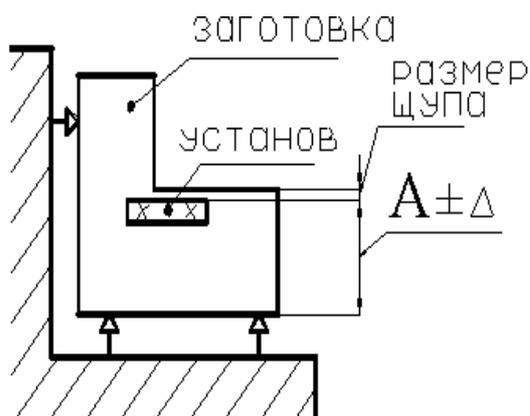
Расчетная схема определения $\varepsilon''_{изг}$ для фрезерных приспособлений
